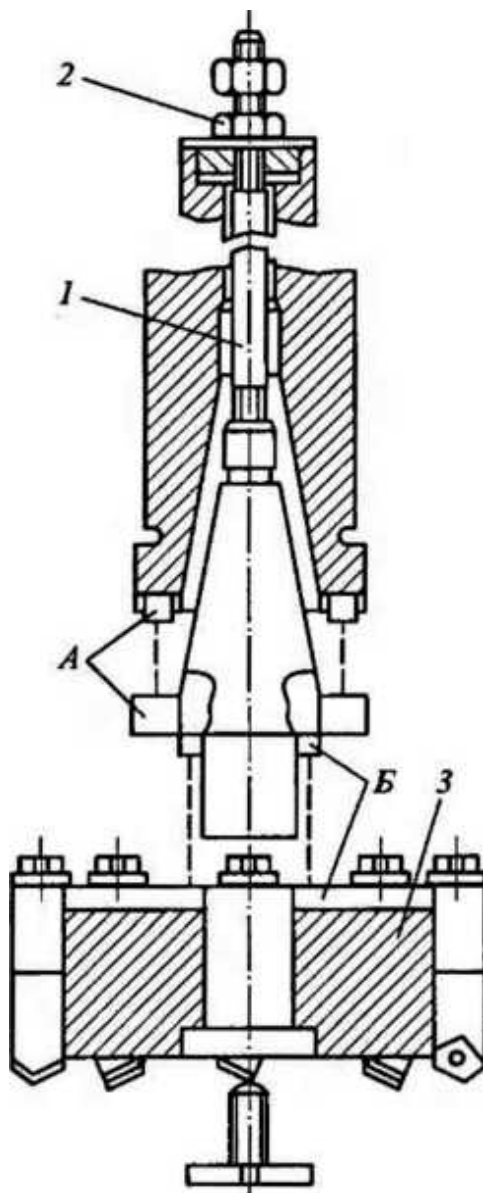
Оправка для концевых и торцевых фрез:
